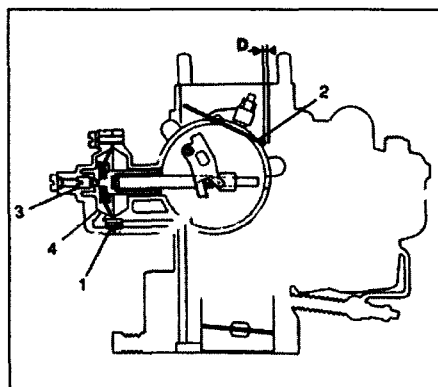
Регулировка вакуумного привода - полуавтоматический привод
